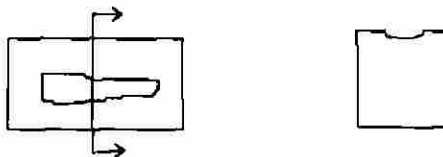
Vista seccional y frontal de un bloque de prueba.
